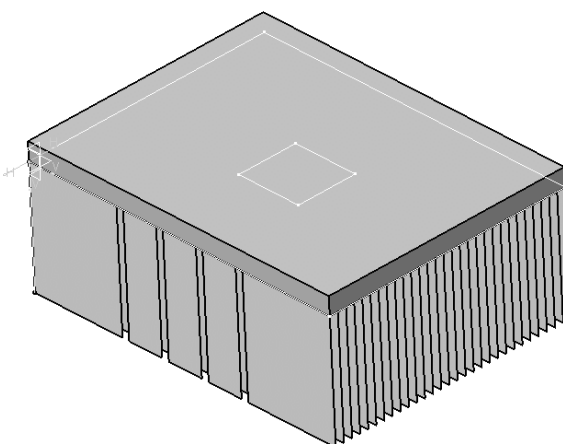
Modelo 3D em CAD do dissipador 11-P4ES-01.
